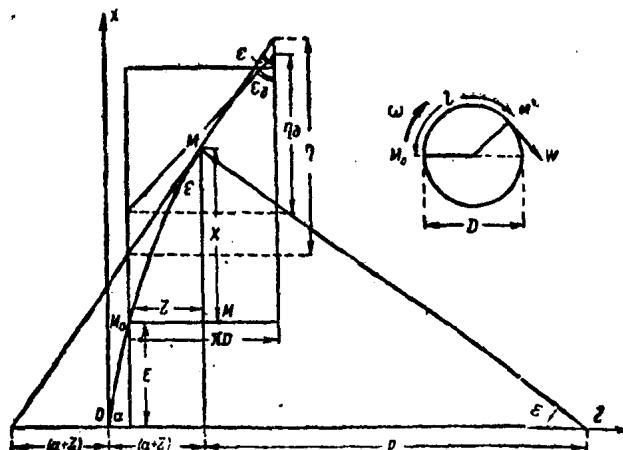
炮膛展开的平面图 (抛物綫形膛綫)
